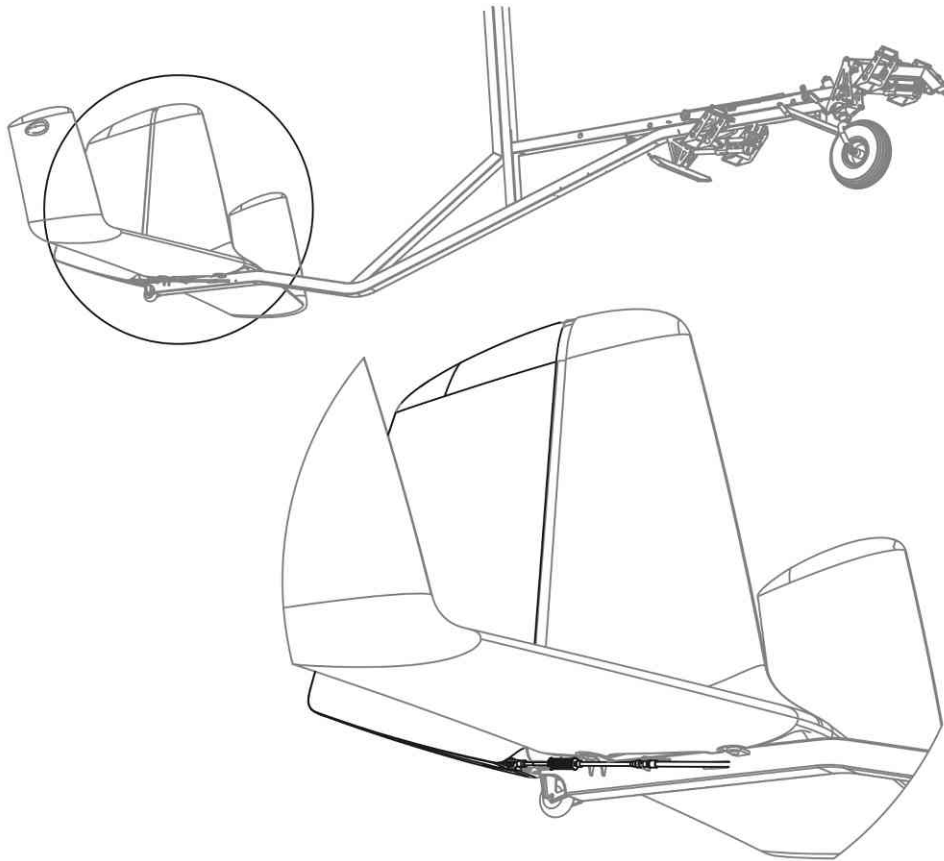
Flugsteuerung - Seitenruder (hinten)
